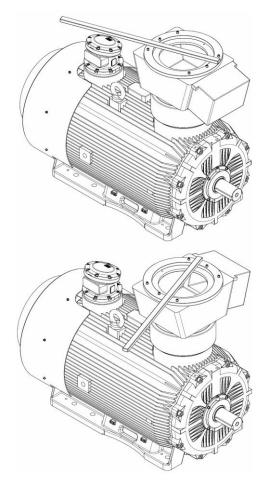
Поворот СКК с помощью поворотного приспособления
